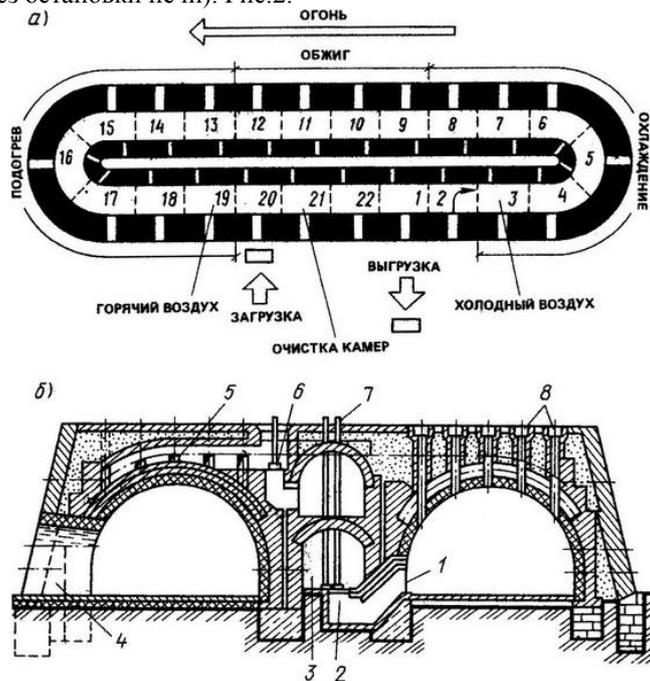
Схема работы (а) и разрез (б) кольцевой печи 1 – дымовые очелки; 2 – дымовой конус; 3 – дымовой канал; 4 – ходок; 5 – рассыпной строй; 6 – клапан рассыпного строя; 7 – штанга; 8 – топливные трубы
